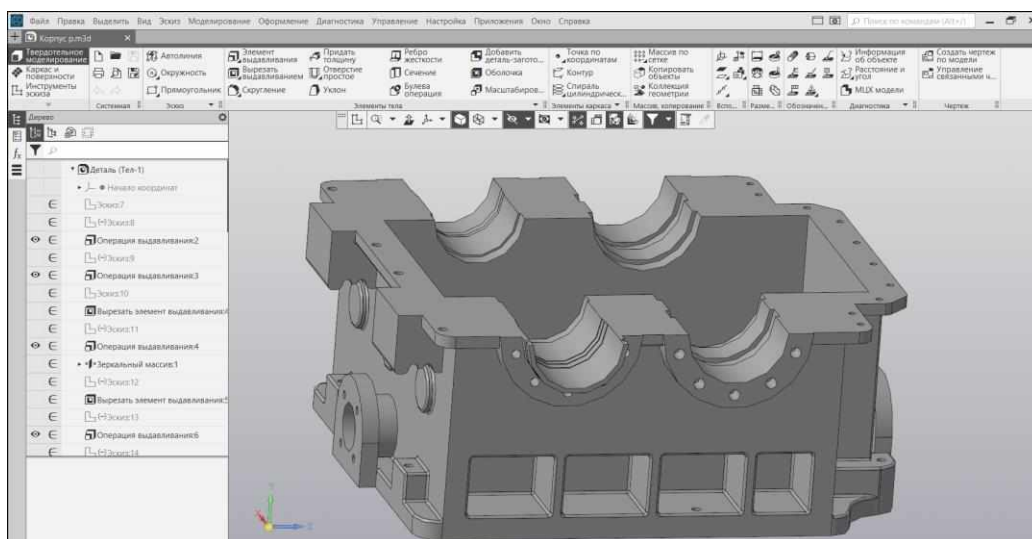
3D-модель корпусу редуктора побудована у середовищі САПР КОМПАС-3D
